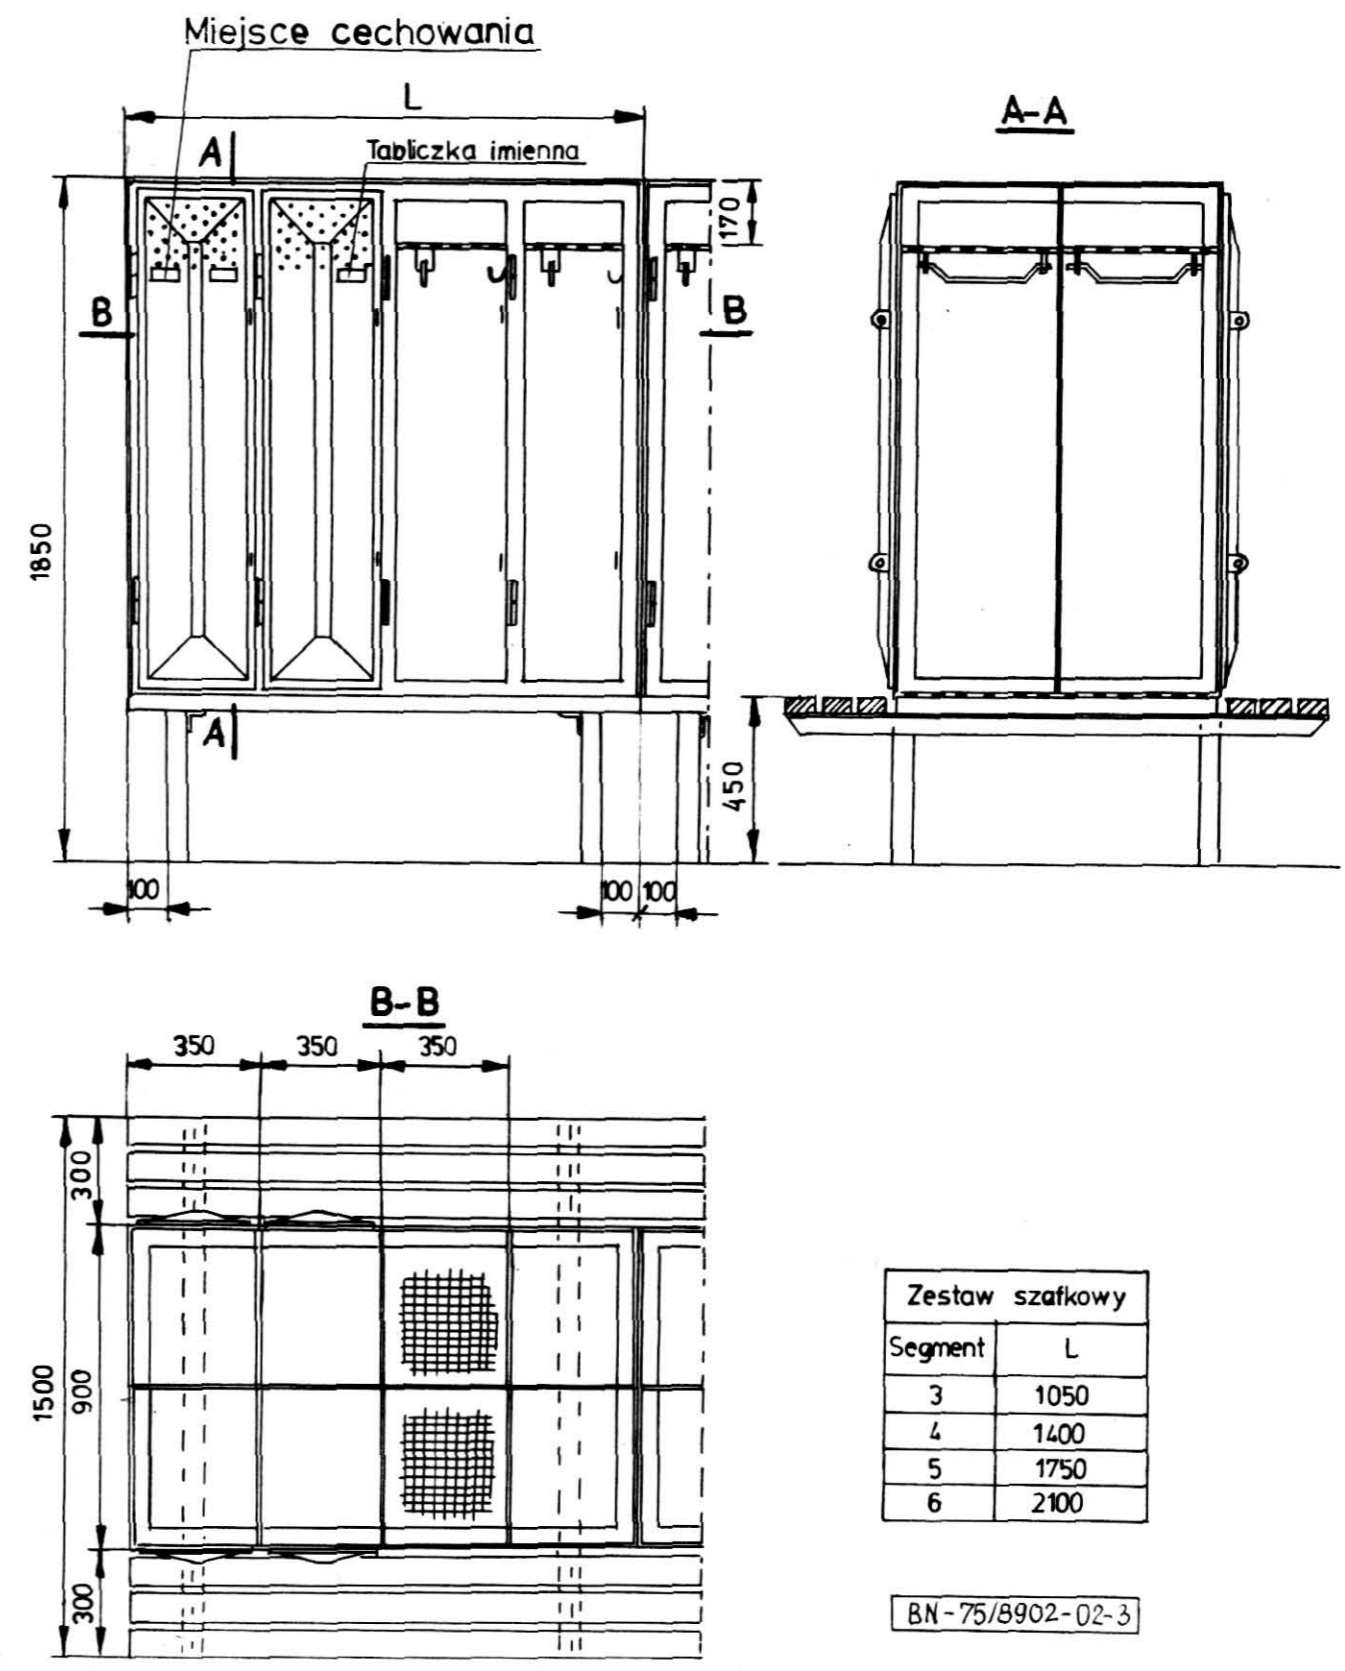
Przykładowa konstrukcja szafki szatniowej typu A
